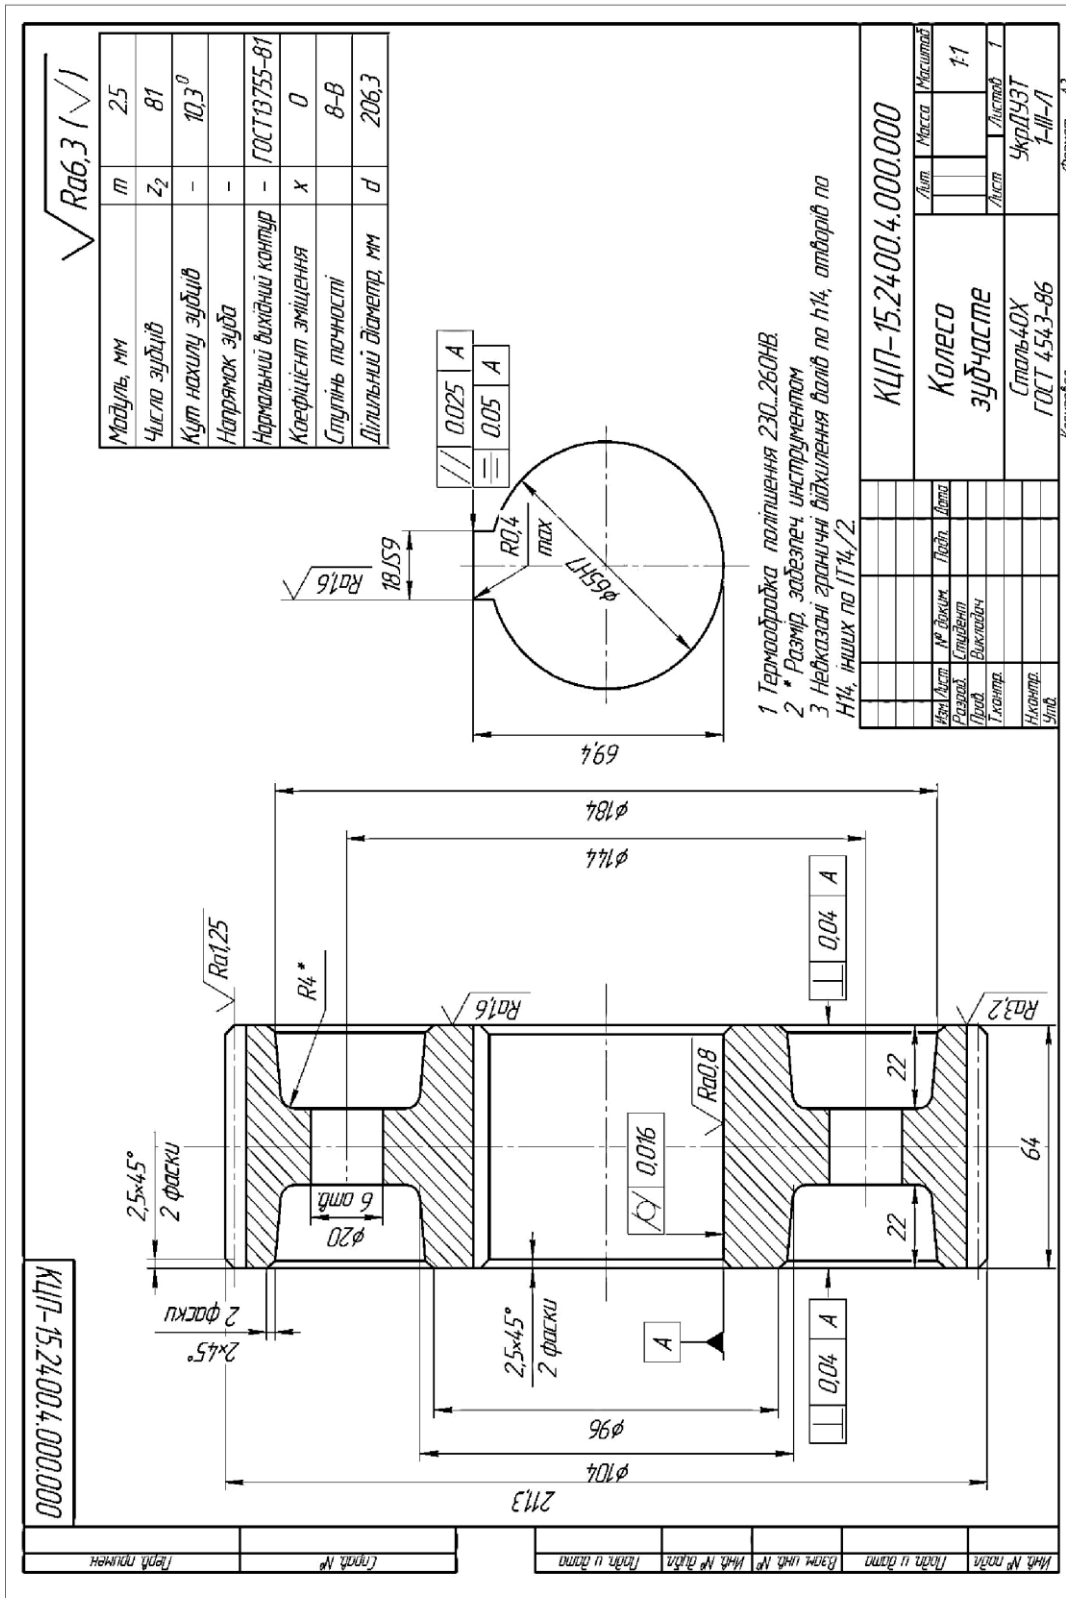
Робоче креслення циліндричного зубчастого колеса
